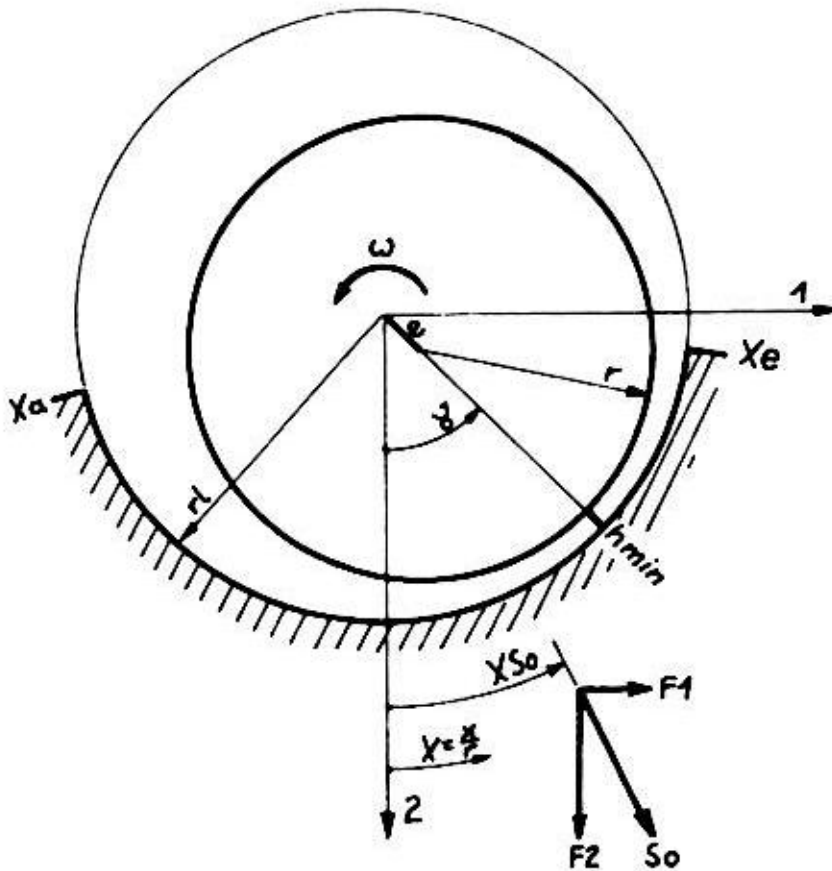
Spaltgeometrie des achsparallelen Lagers mit kreisrunder Welle und kreisrunder Lagerschale
